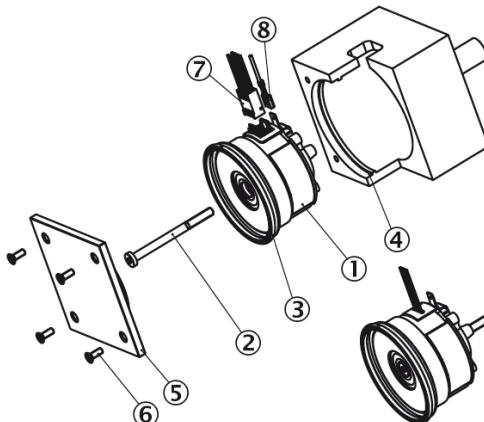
plan de montage SRS50S/SRM50S arbre conique, bielle caoutchouc
